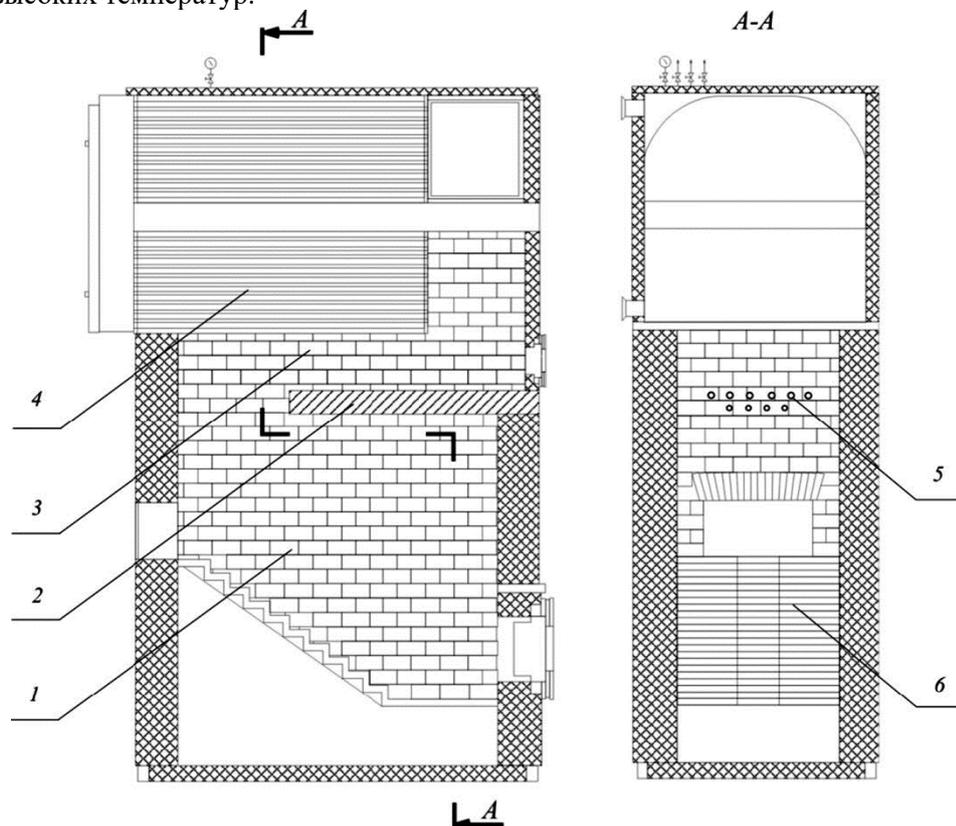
Устройство твердотопливного водогрейного котла КВУ-2000: 1 – топка; 2 – арочный свод; 3 – камера дожига; 4 – двухходовой газовойодяной теплообменник; 5 – сопла вторичного воздуха; 6 – колосниковая решетка
